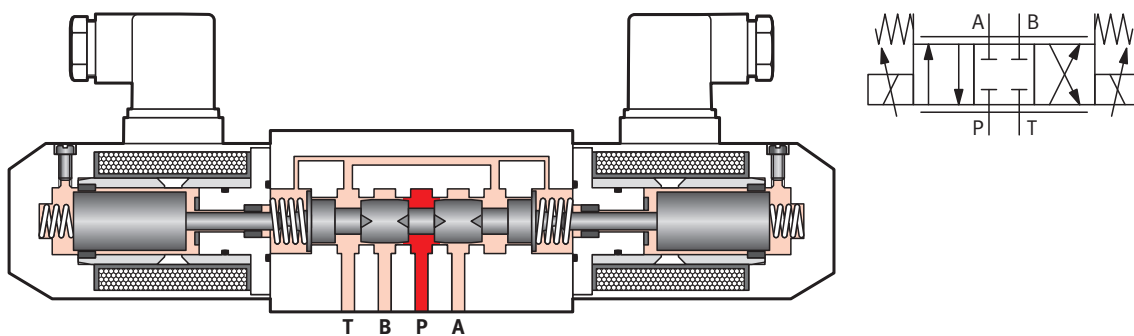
válvula posicionadora sin regulación de la posición. Vista en corte y símbolo.
